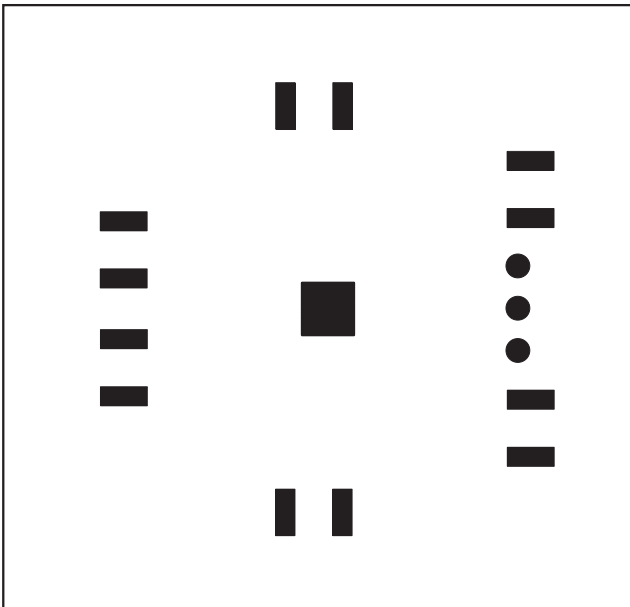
MAX9985评估板PCB布局—底层阻焊层
